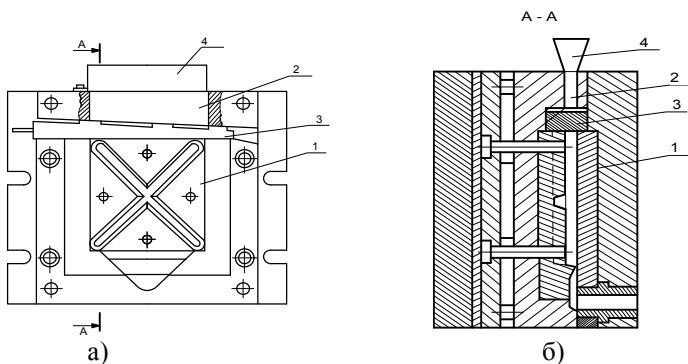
а) Конструкция пресс-формы: 1 – рабочая полость; 2 – загрузочное отверстие; 3 – запирающий клин; 4 – направляющая воронка б) Сечение А-А
